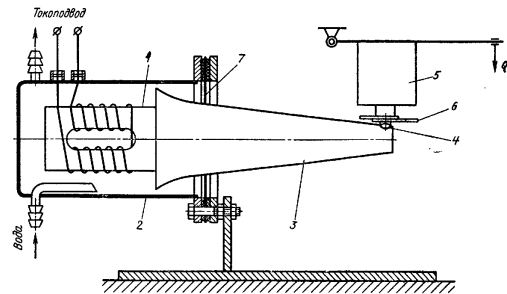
Схема установки для точечной сварки ультразвуком
